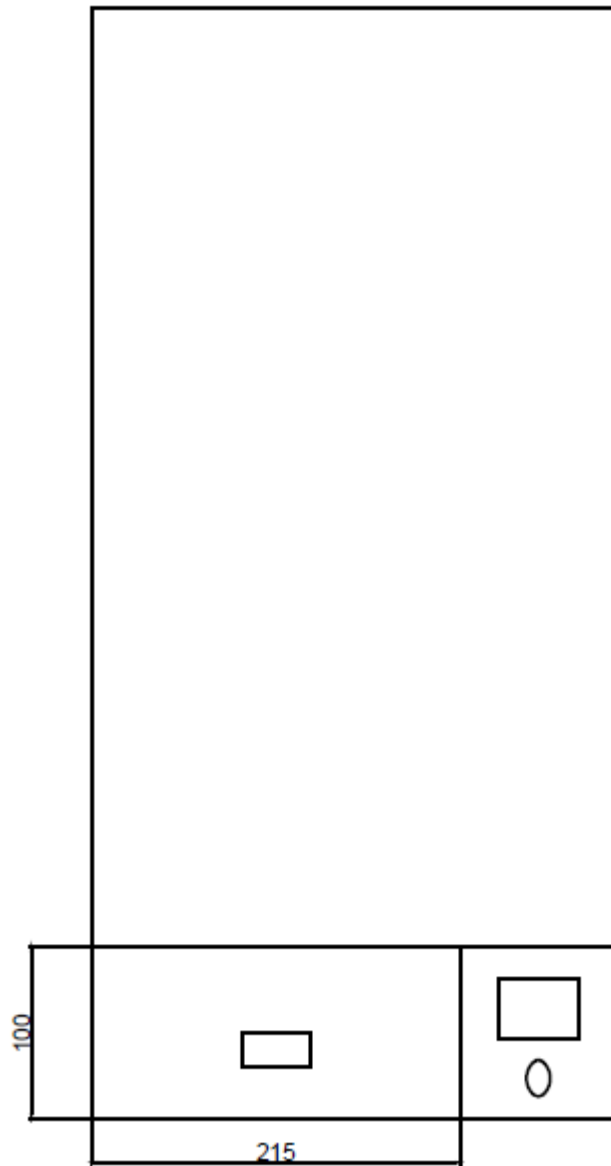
dimensões da porta de acesso, cotas em milímetros
